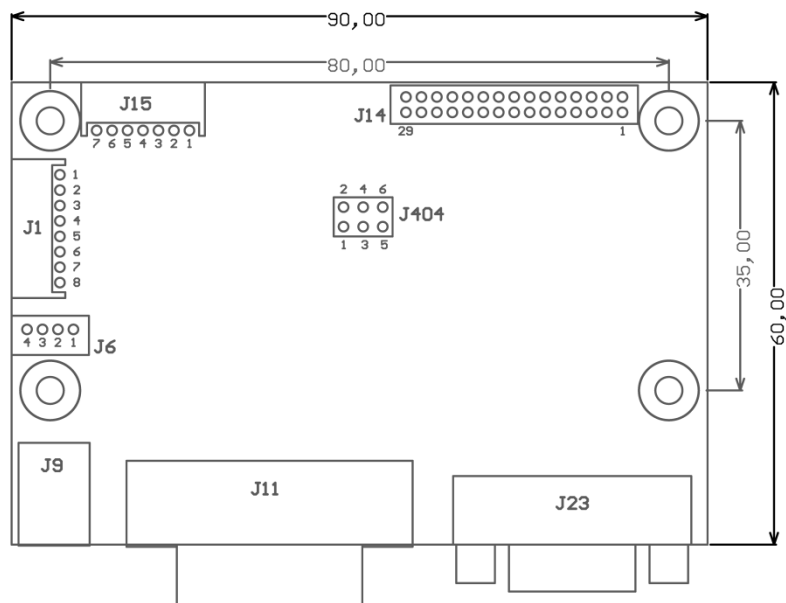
Габаритный чертёж контроллера УКМ-1912-01
